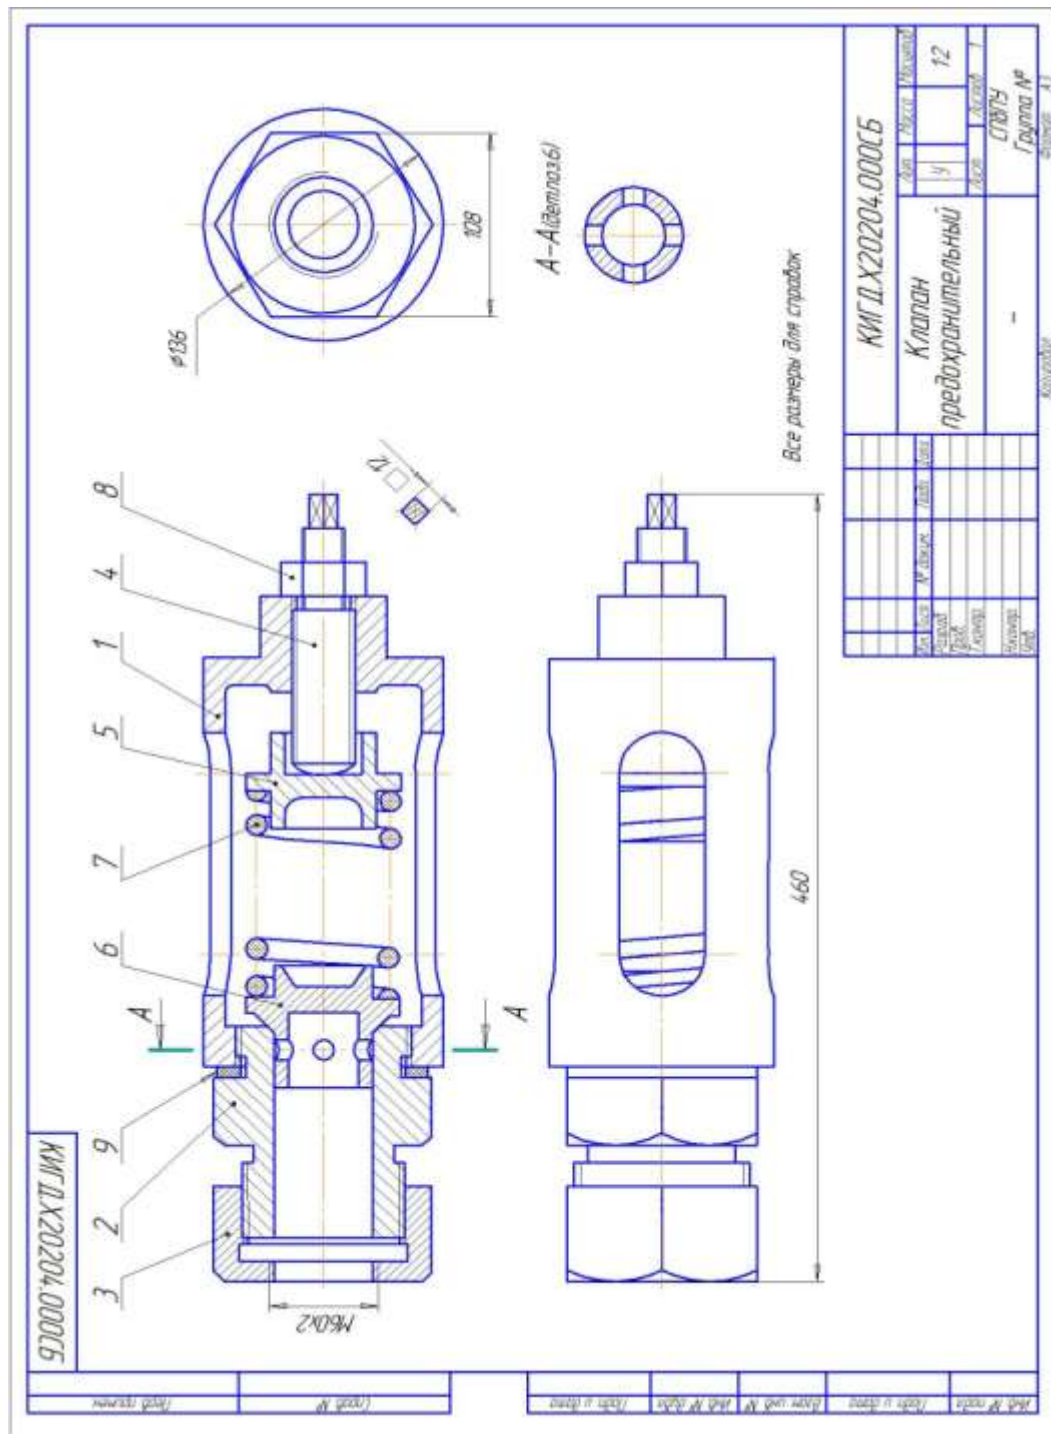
Сборочный чертеж «Клапан предохранительный»
